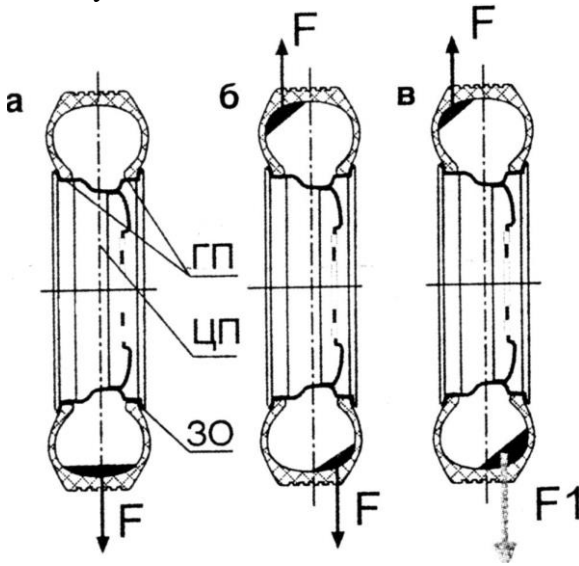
Види дисбалансу колеса: ЦП - центральна площина обертання колеса; ГП - горизонтальна поверхня обода; ЗО - закраїни обода
